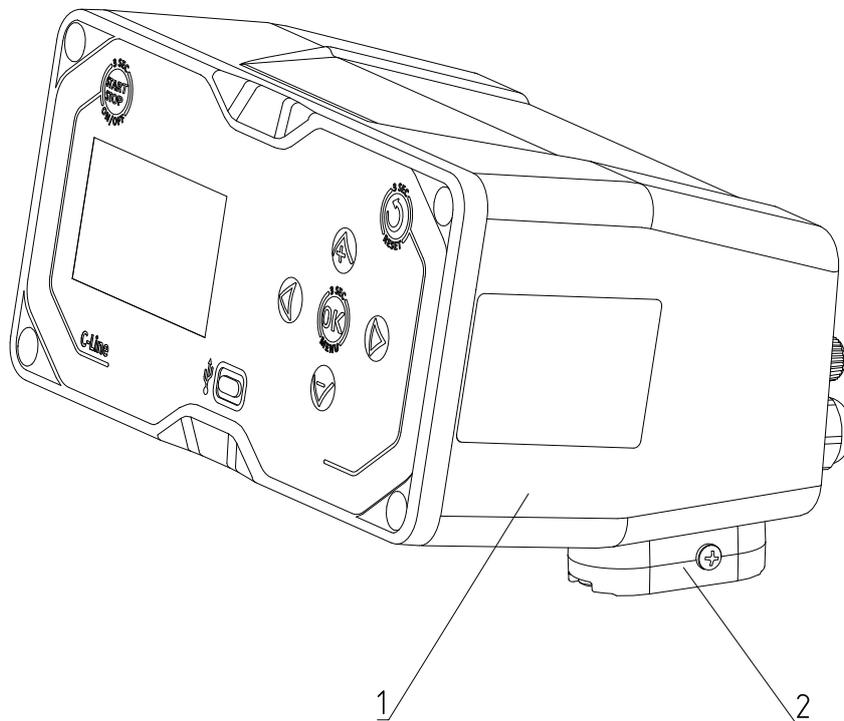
Внешний вид контроллера C-Line 200SF с фиксатором крепления
